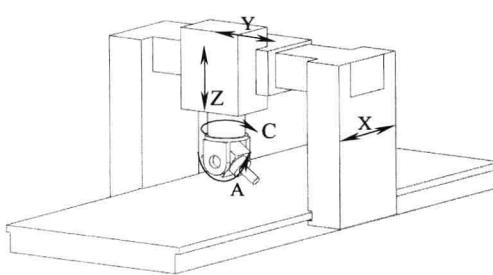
主轴倾斜型五轴联动数控机床结构原理
